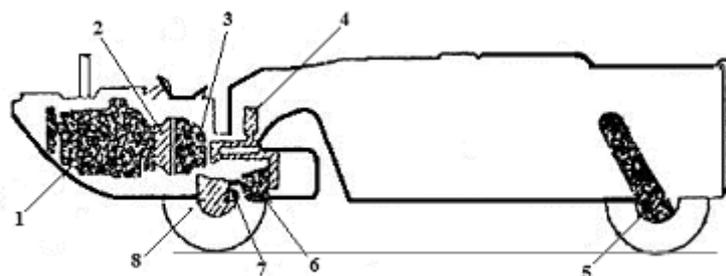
Схема расположения тяговых агрегатов двухзвенного поезда ХМ-437: 1 – дизель GMC; 2 – генератор; 3 – сцепление; 4 – электропривод рулевого управления; 5 – электродвигатели задних колес; 6 – коробка передач; 7 – дифференциал; 8 – раздаточная коробка
